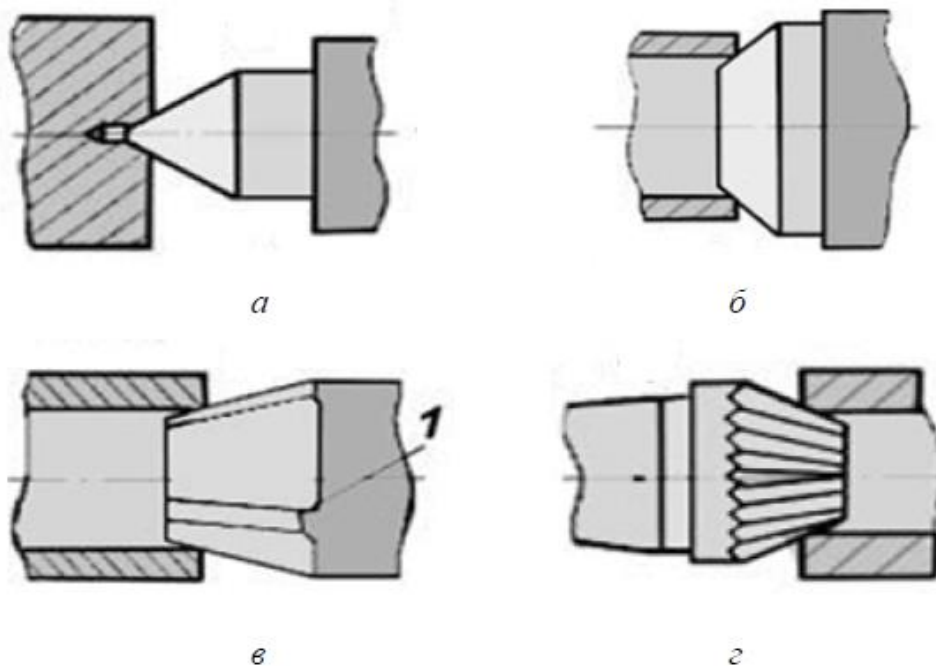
Схемы установки заготовок на основе применения жестких центров:
